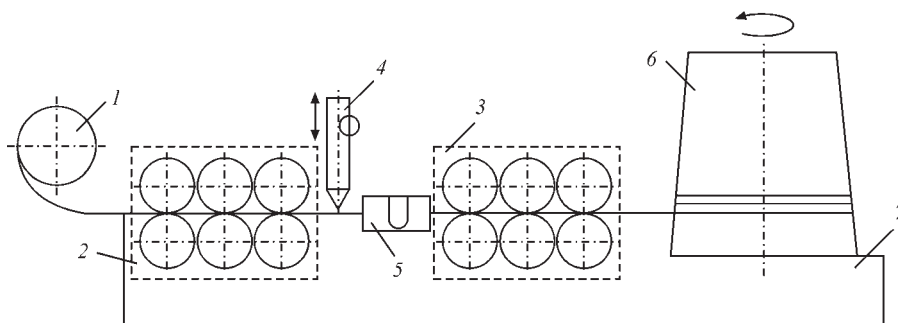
Схема волочильного верстата для виробництва порошкового титанового дроту: 1 – касета; 2, 3 – роликів кліт; 4 – дозатор; 5 – U-подібна планка; 6 – барабан; 7 – станина
